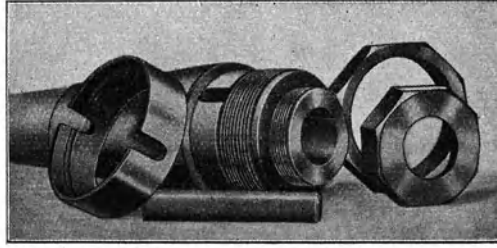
Die einzelnen Teile der Fräsdornbefestigung.
